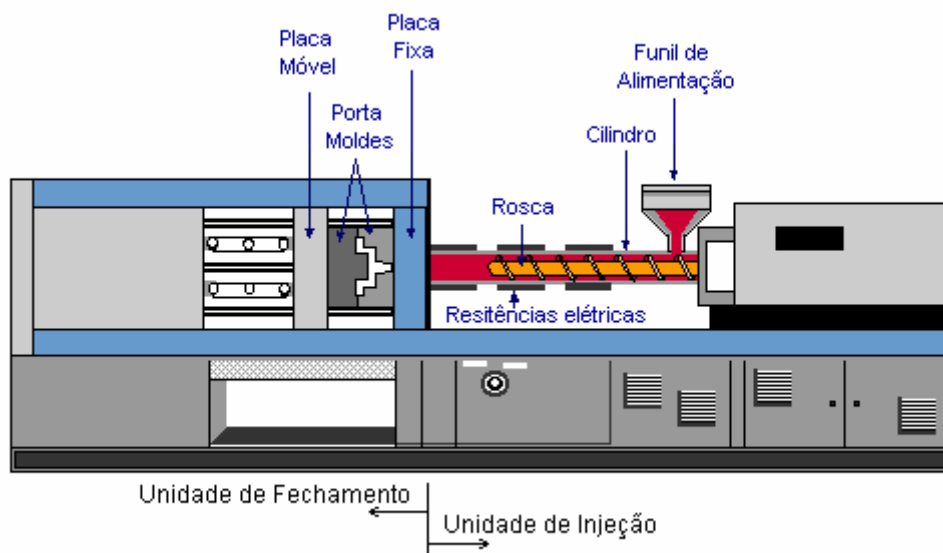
Máquina injetora e componentes das unidades de fechamento e de injeção. (C-MOLD DESIGN GUIDE, 1991)
